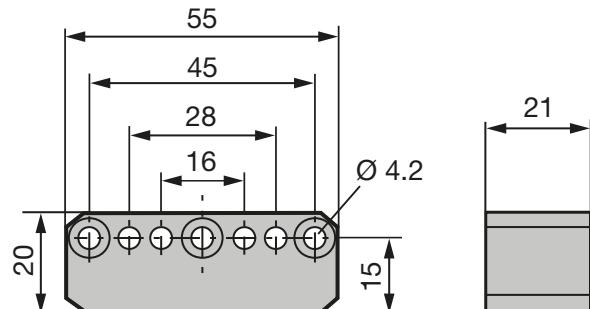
Dimensions de montage du capteur de position BTL5-P-5500-2
